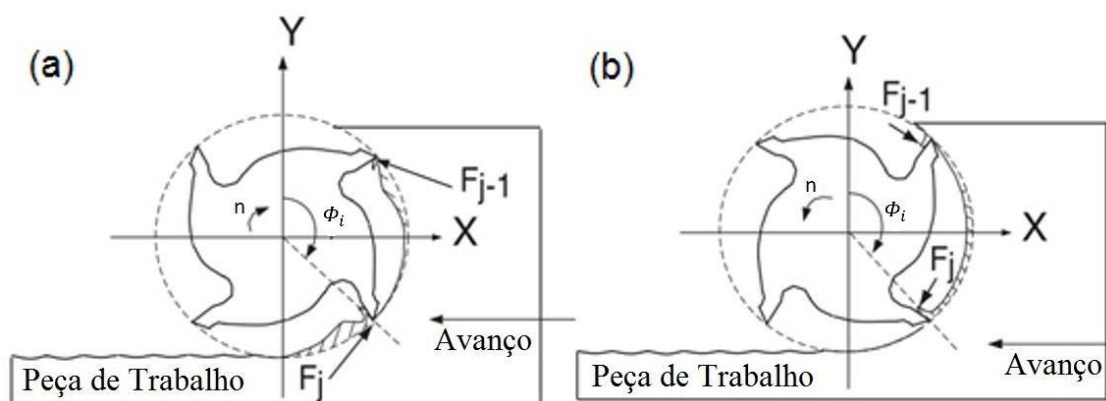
(a) Fresamento concordante – downmilling/Climb milling e fresamento discordante - upmilling; (b) [18]
